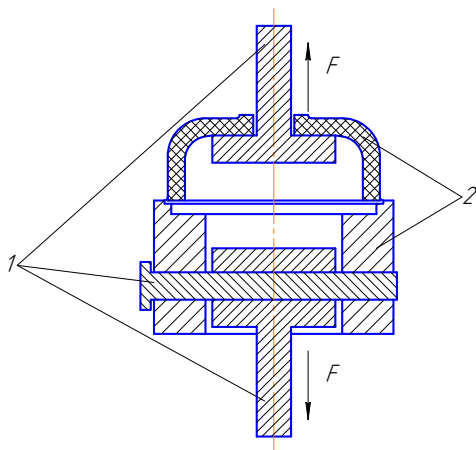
Схема прочностного испытания металлокерамического паяного образца: 1 – стержни захвата; 2 – паяный образец
